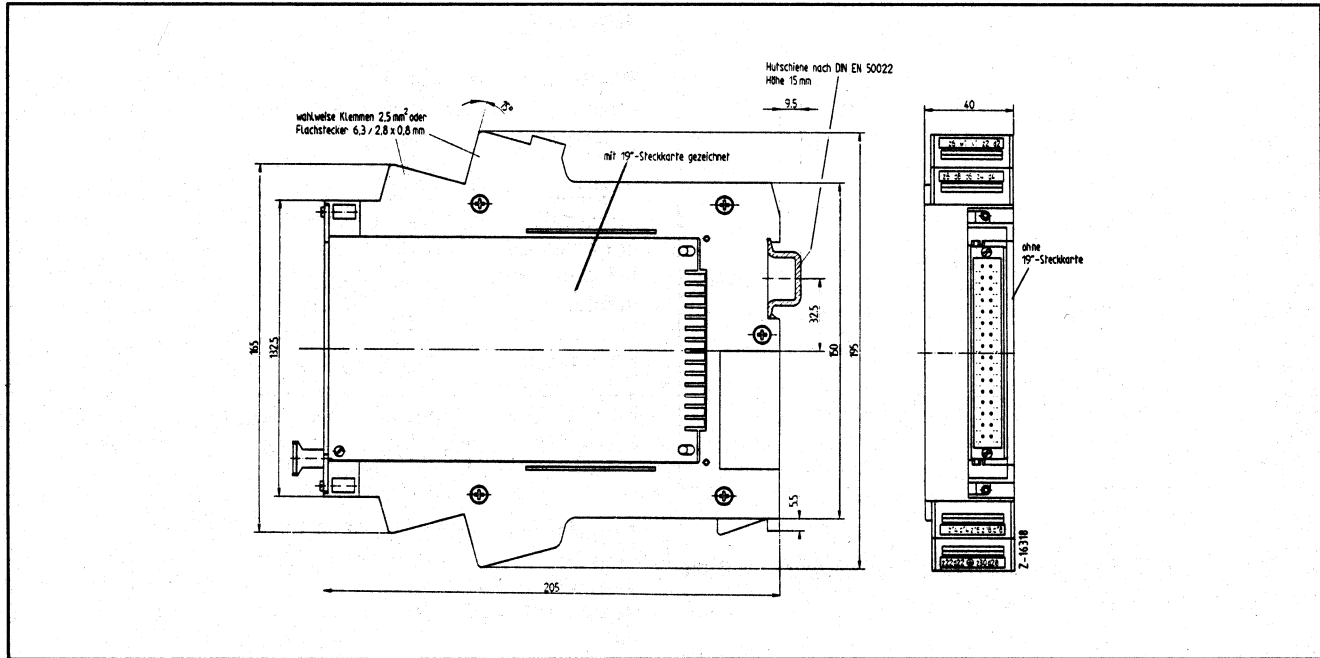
Maßbild Aufbaugehäuse IP 20 (Maße in mm)
